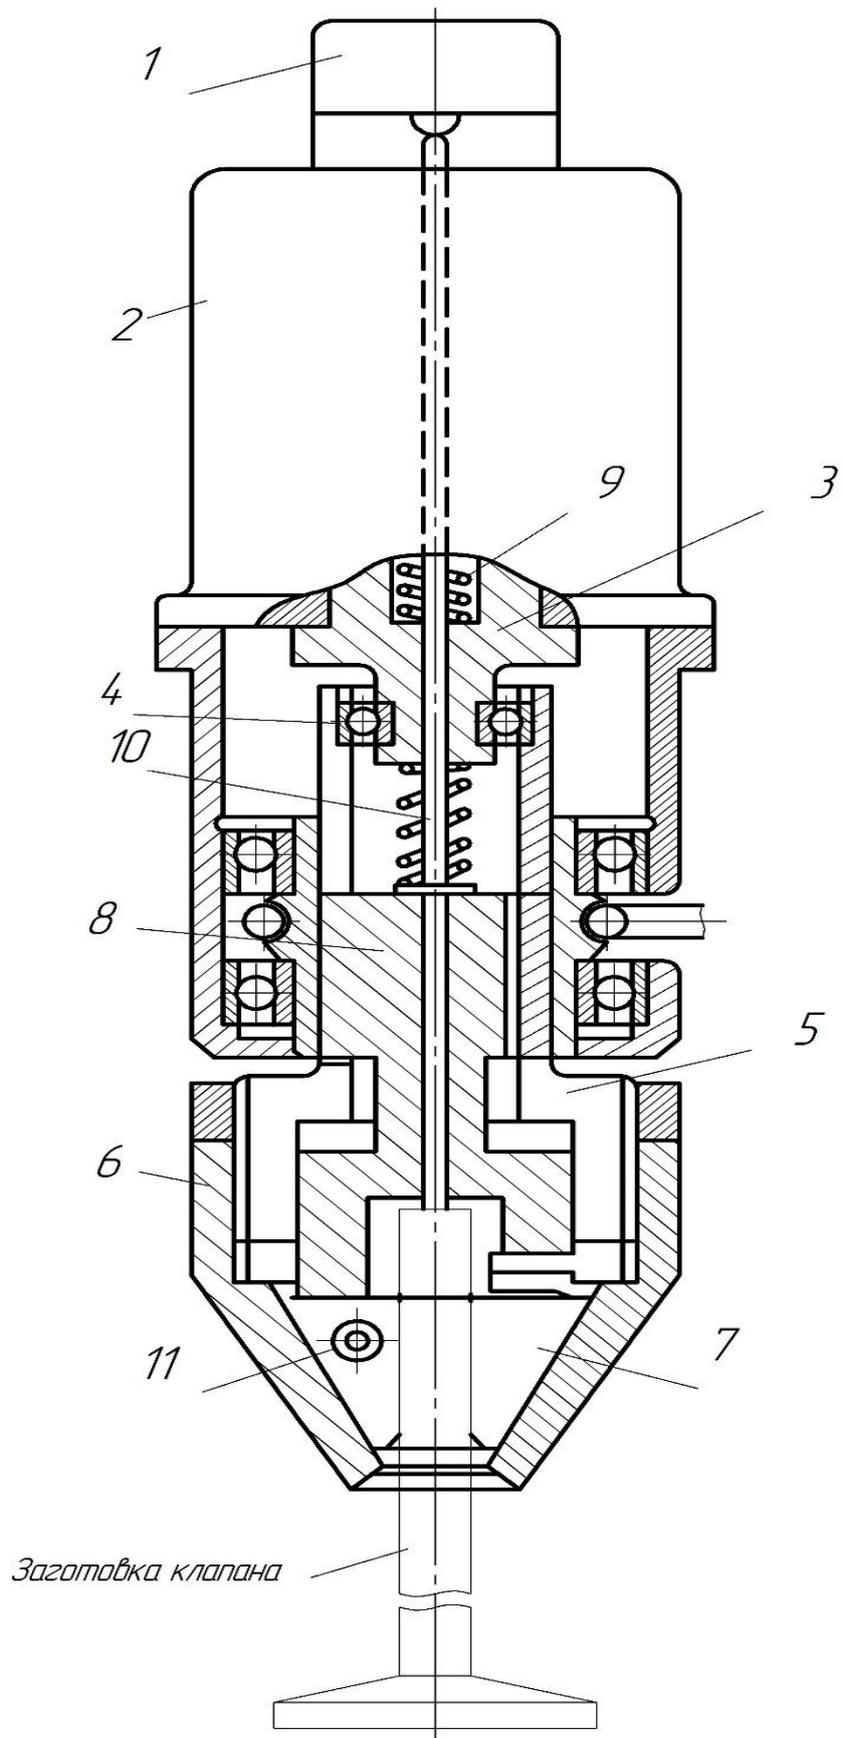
Затискний механізм установок для наплавлення клапанів
